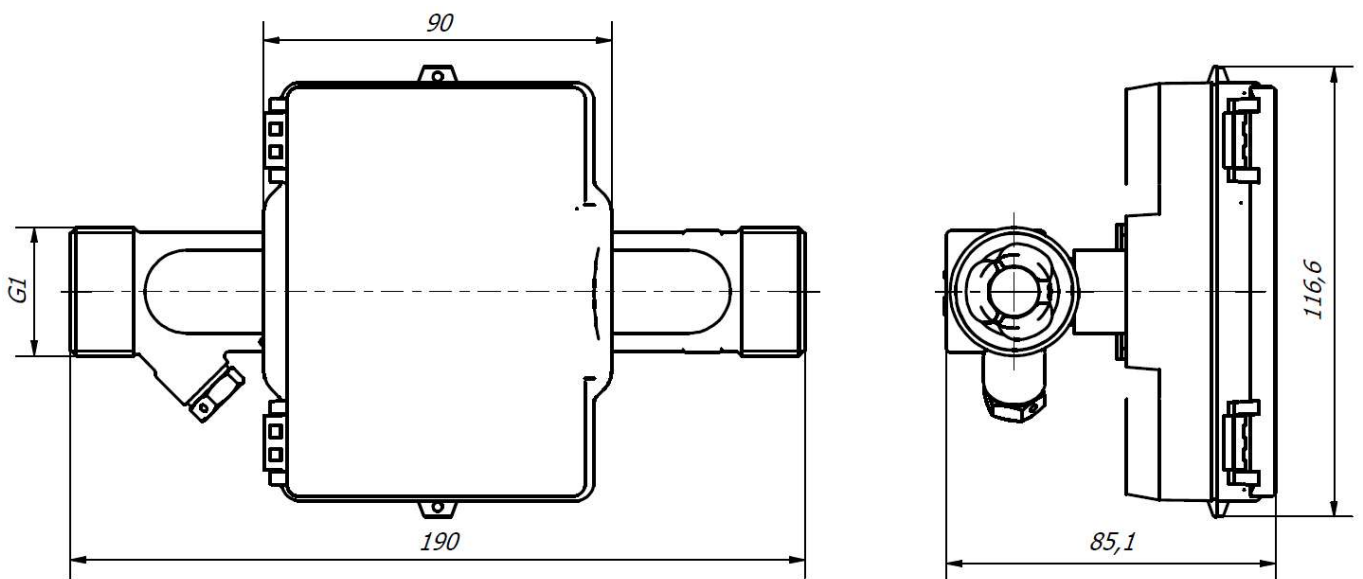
Gjengede endetilkoblinger G1", monteringslengde L=190 mm.
